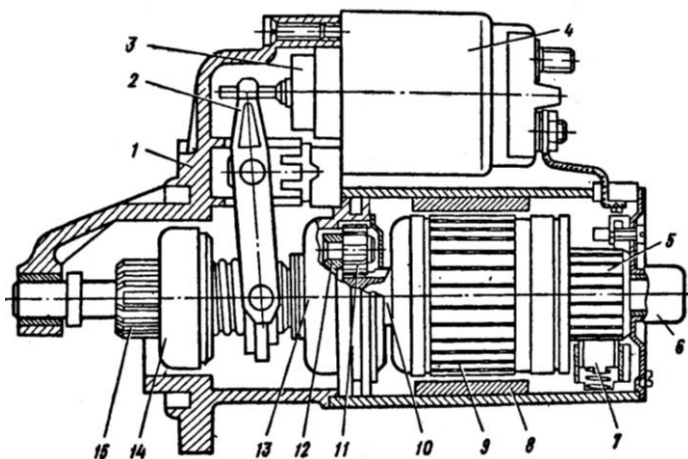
Стартер с планетарным редуктором и возбуждением от постоянных магнитов:
